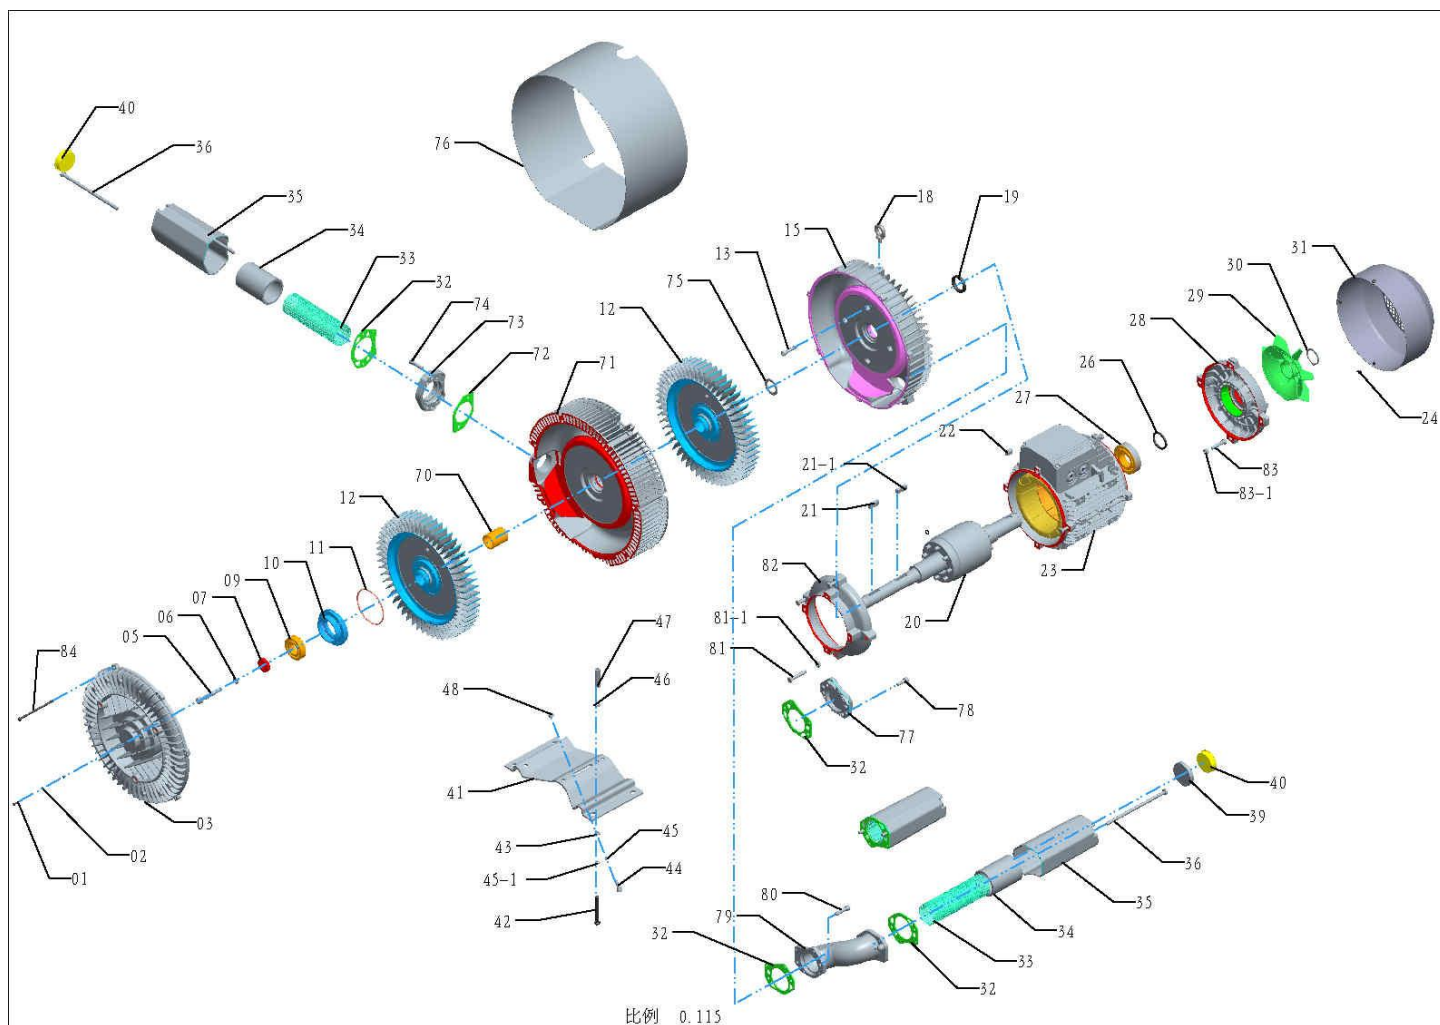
Деталировка двухступенчатых воздуховок 2RB
